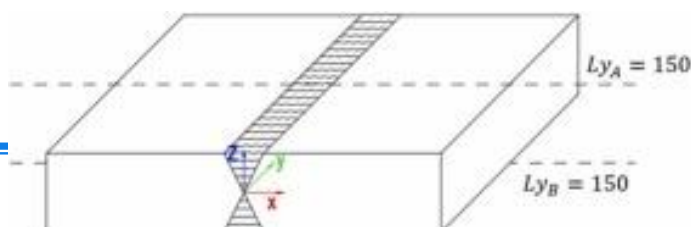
Поперечное направление через центр сварного шва (мм)
